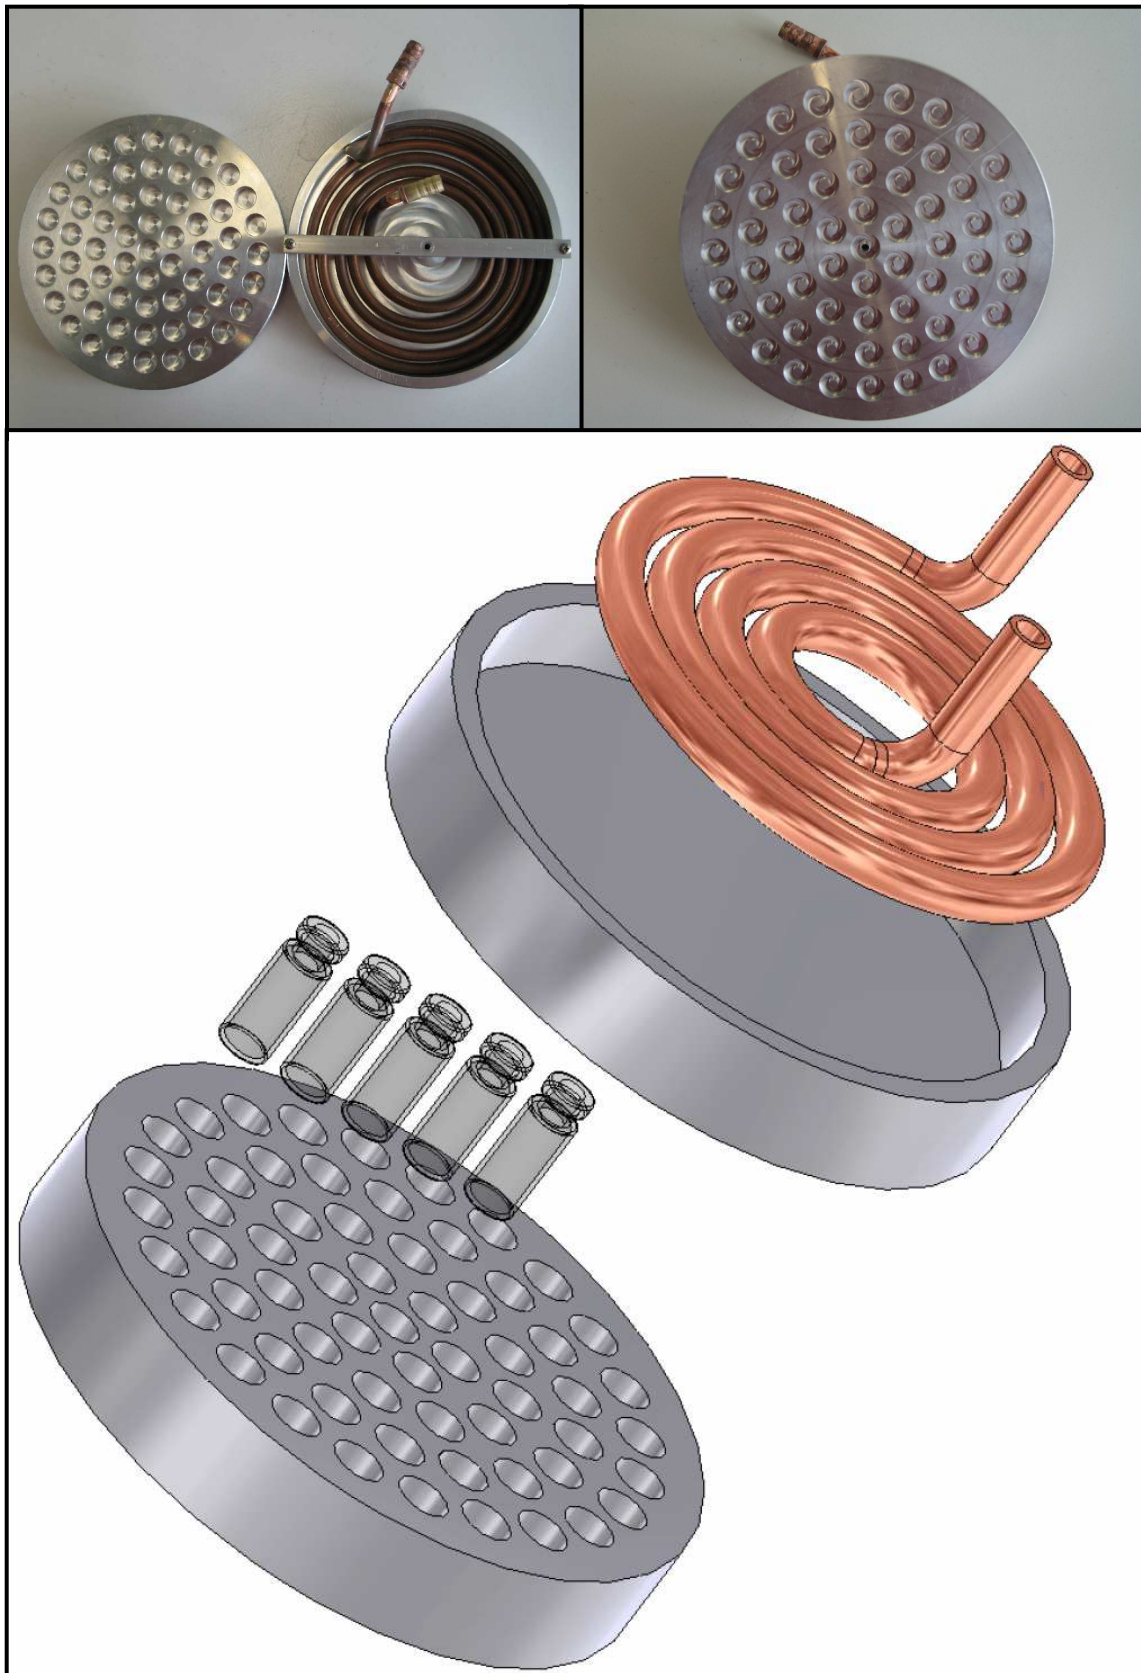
Bilder und Explosionszeichnung des entwickelten Reaktorblocks.
